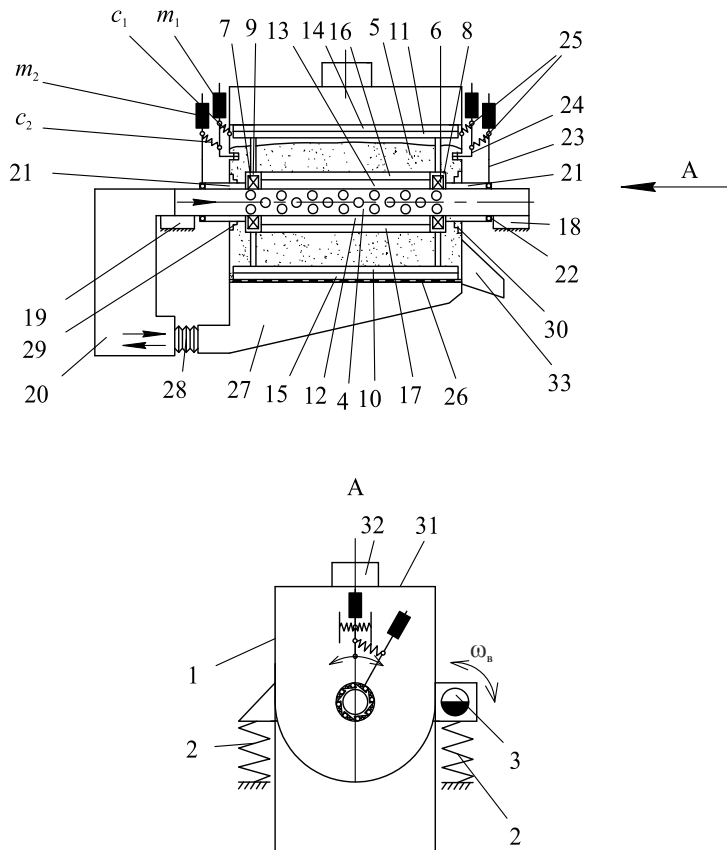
Віброозонуюча сушарка з перемішувачими лопатями і маятниковими механізмами вільного ходу: 1 — камера U-подібної форми; 2 — пружини; 3 — вібробудувач; 4 — газорозподільна решітка; 5 — зернова сировина; 6, 7 — корпуси підшипників; 8, 9 — підшипники; 10—13 — лопаті-перемішувачі; 14-17 — еластичні скребки; 18, 19 — опори; 20 — система подачі-відбору сушильного агента; 21 — втулка; 22 — маятникові механізми; 23, 24 — маятники; 25 — пружини; 26 — перфороване днище; 27 — дифузор; 28 — еластичне з'єднання; 29, 30 — пружні вставки; 32 — завантажувальний отвір; 33 — розвантажувальний лоток
